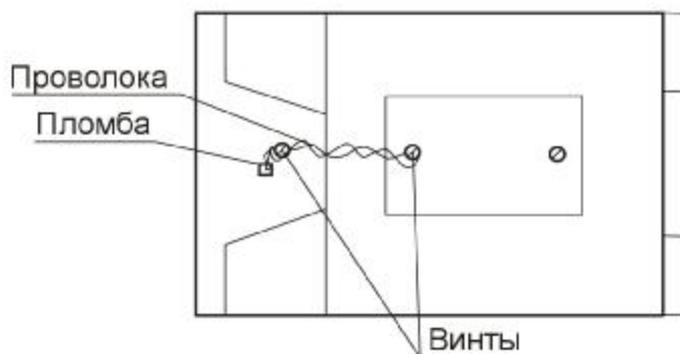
Схема пломбировки вторичного преобразователя при креплении на DIN-рейку.
